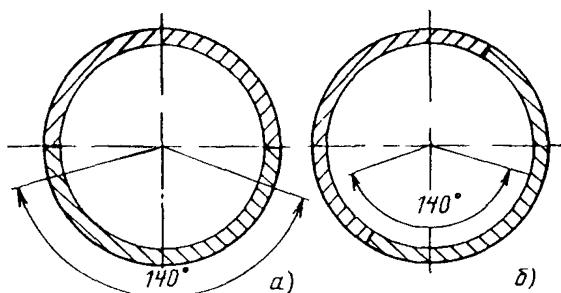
Расположение сварных швов в нижней части оборудования и трубопроводов
